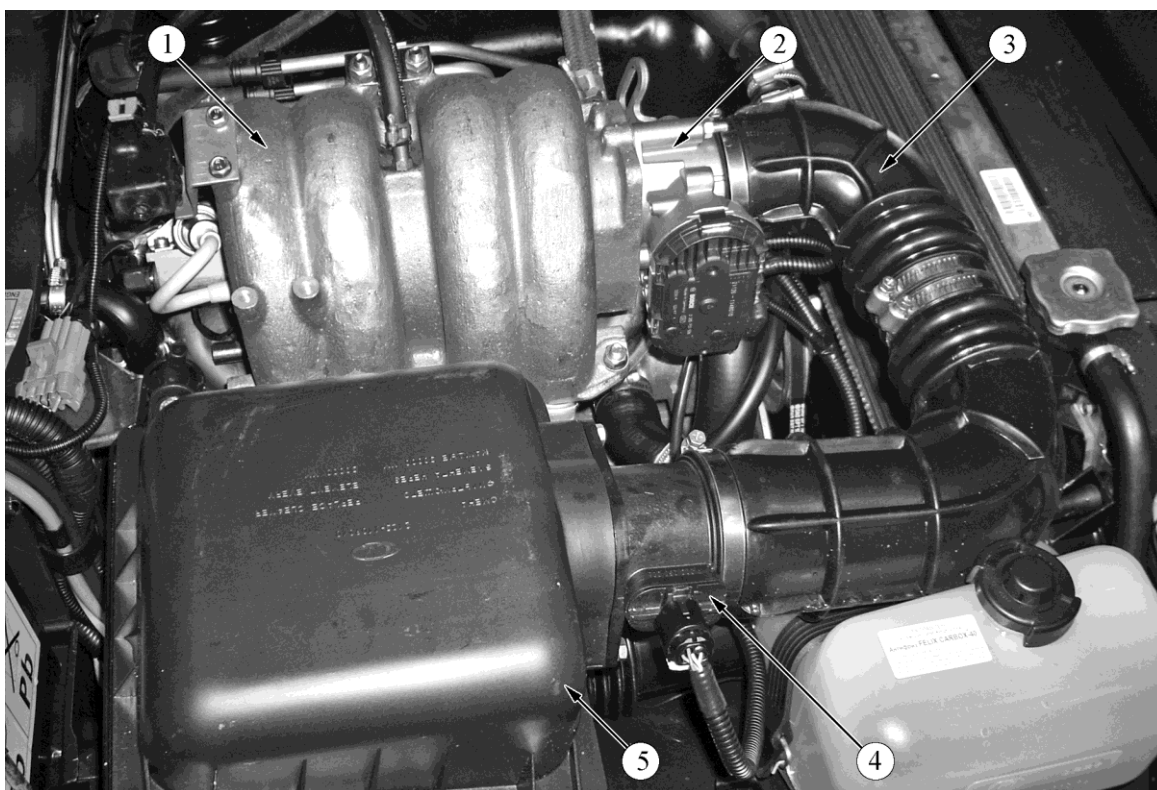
Система впуска воздуха двигателя 21126:
